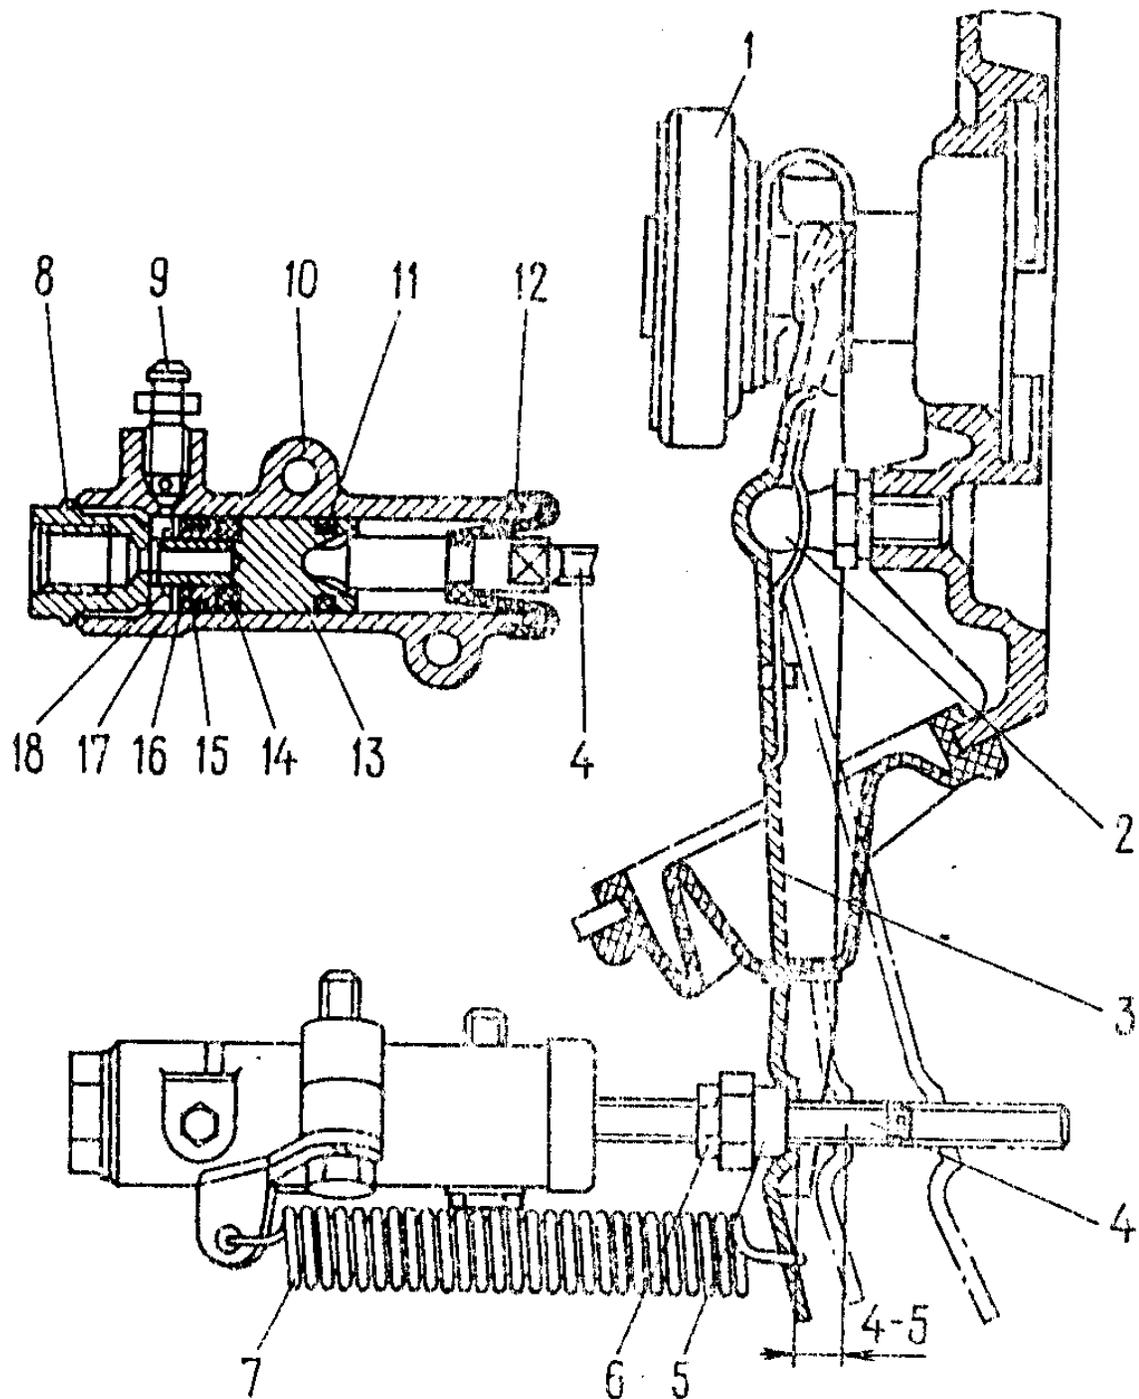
Cilindro de trabajo y horquilla de desembrague:
